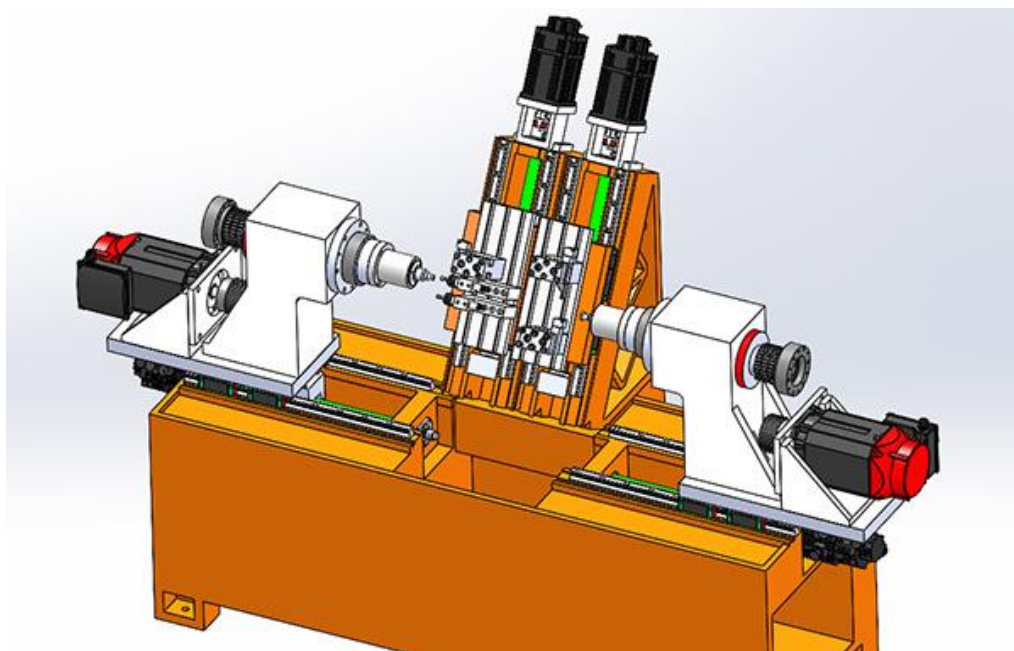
Компонування токарного верстата з ЧПК моделі NC36S1
